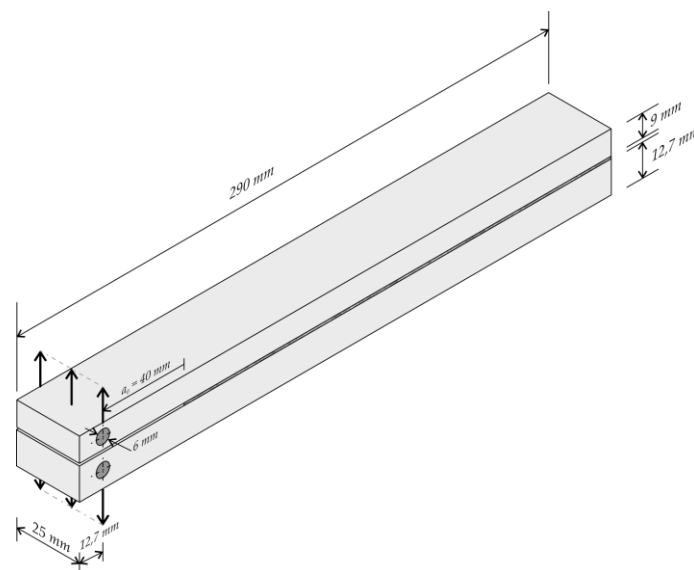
Geometria do ensaio ADCB (dimensões em mm) [36]
